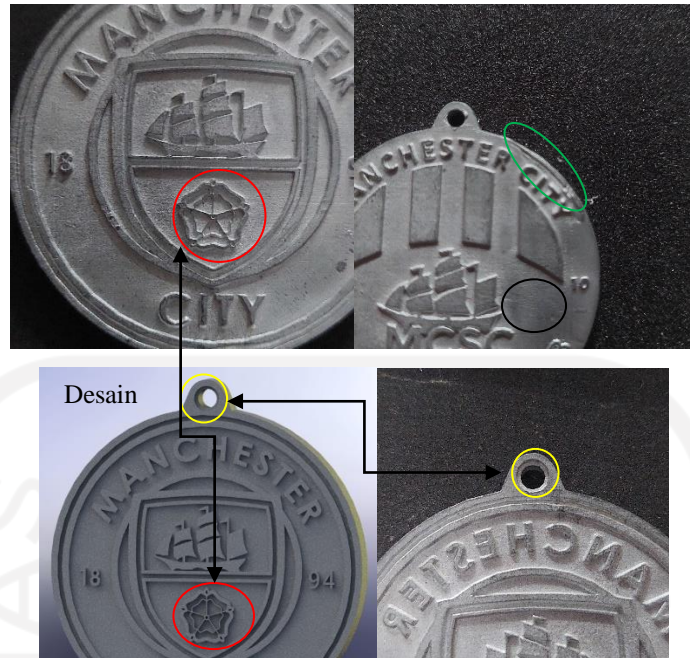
21 Hasil *Spin Casting* (CW, 800 rpm)
